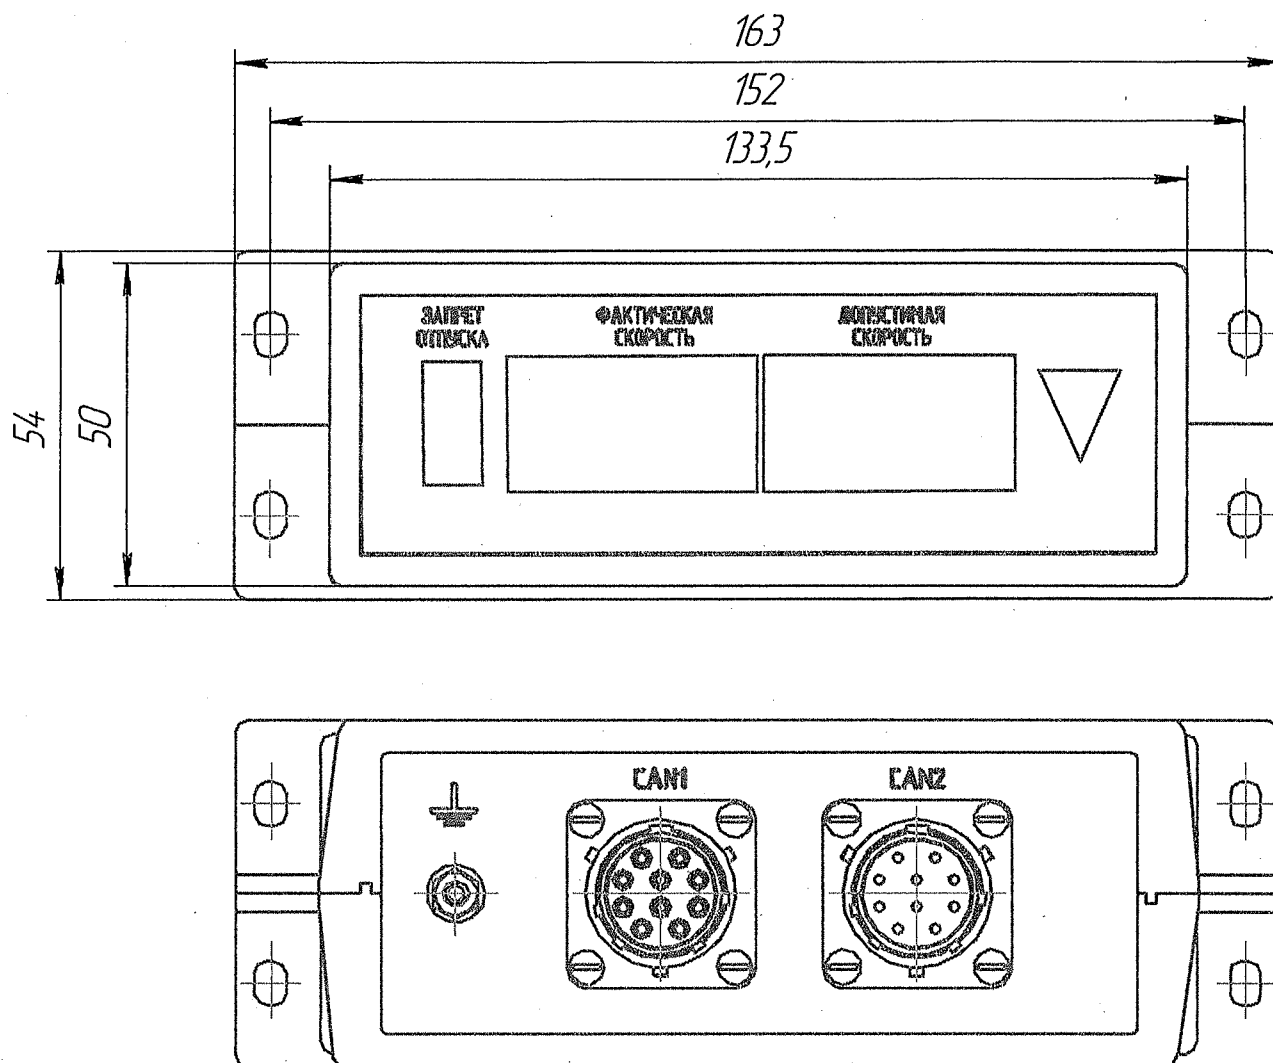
Внешний вид и присоединительные размеры блока БИЛ-ИП-05
